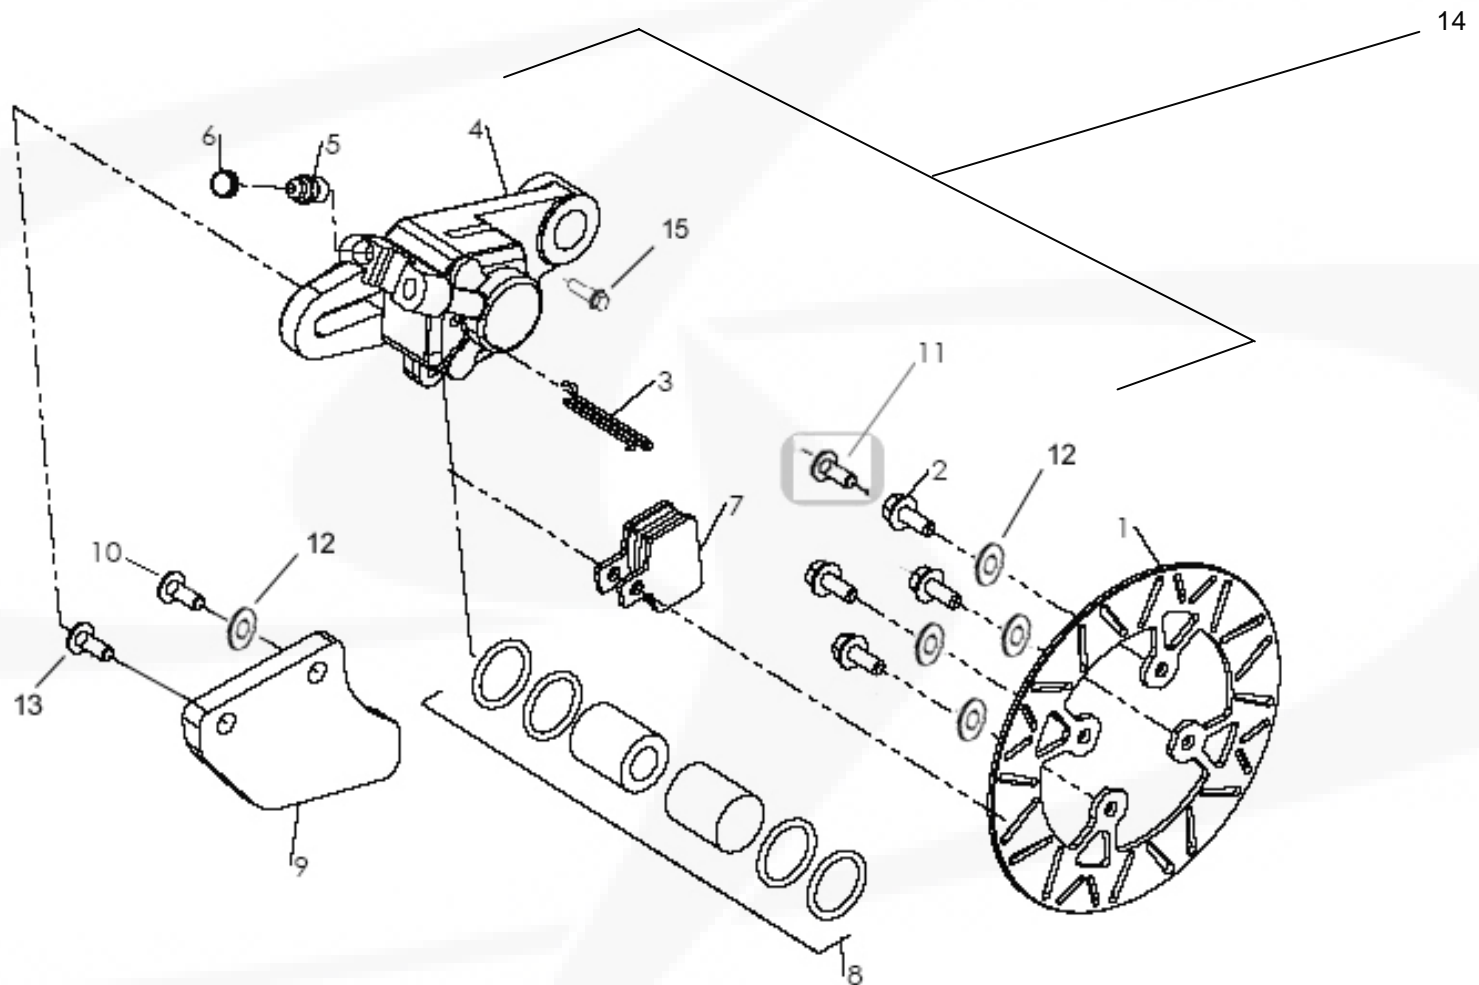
FREIN ARRIÈRE / REAR BRAKE / FRENO TRASERO
